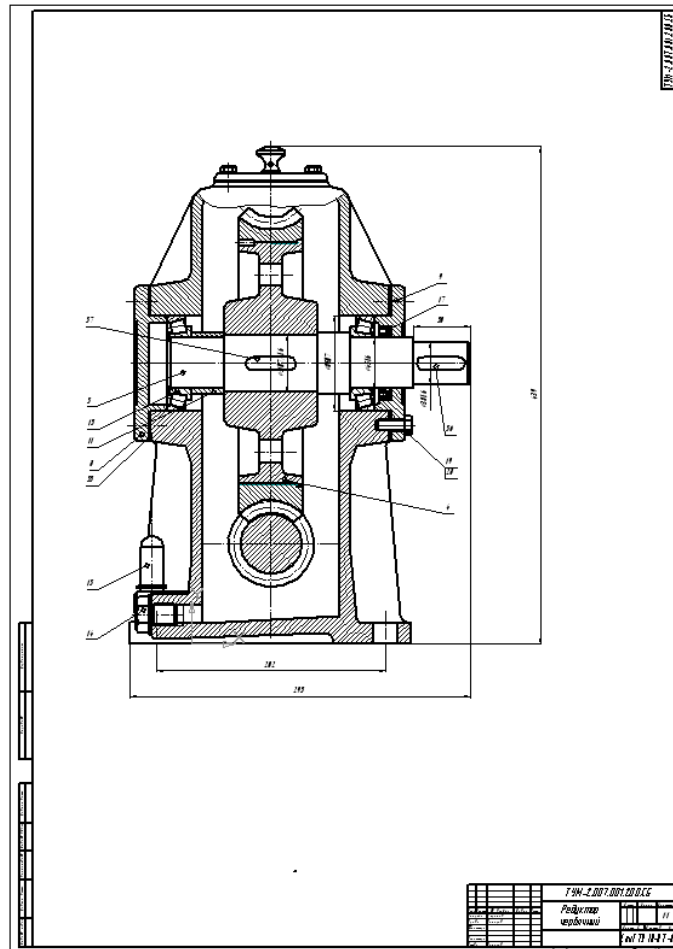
Пример сборочного чертежа червячного редуктора (вид сбоку)
